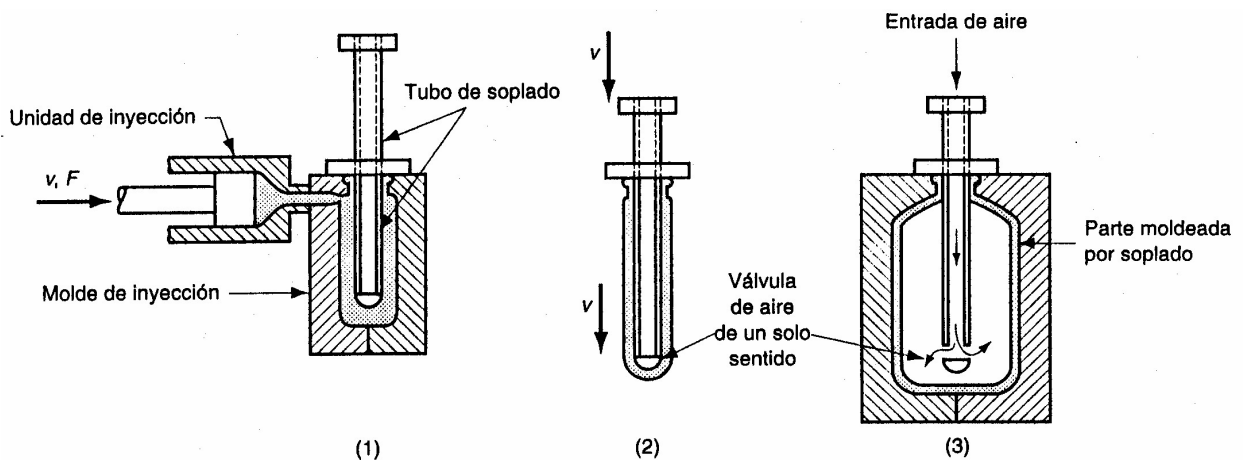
Moldeo por extensión y soplado: (1) moldeo por inyección del paríson, (2) extendido y (3) soplado.
